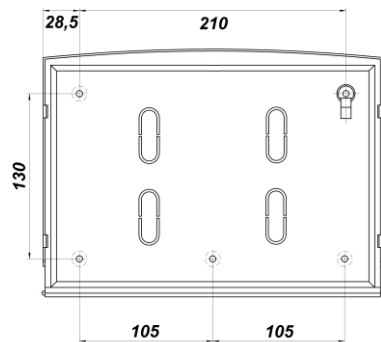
Розмітка отворів для кріплення корпусу ПКІ
